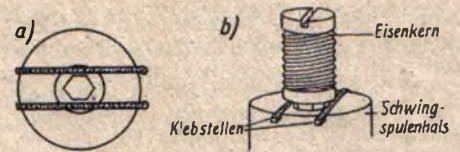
Befestigung des Eisenkerns; a) durch die Schwingenspule, b) seitlich gesehen
